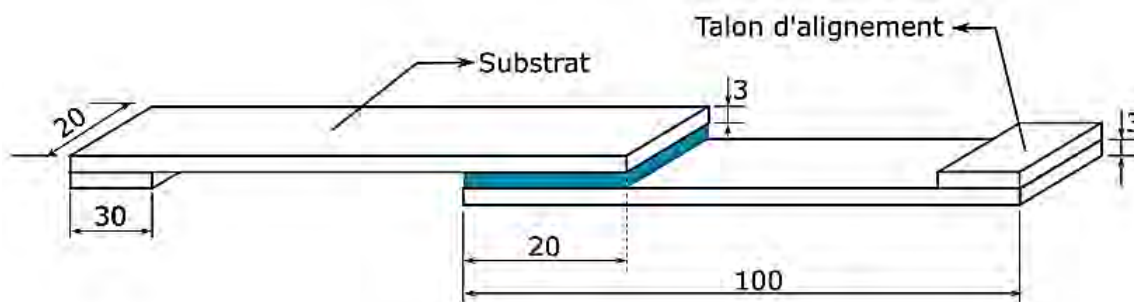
Géométrie et dimensions des éprouvettes du type SLJ.
